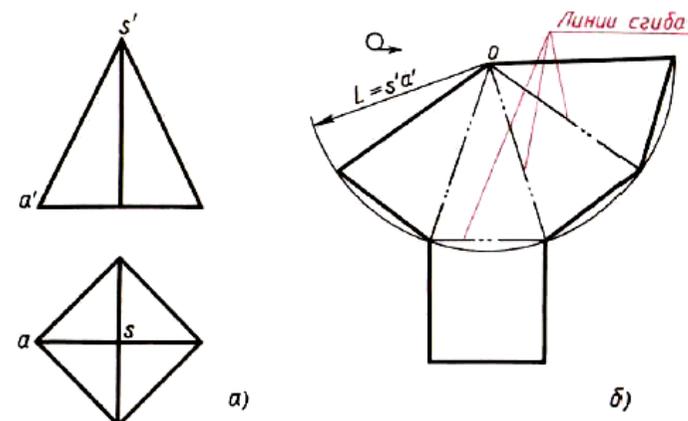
Построение чертежа развертки поверхностей пирамиды:
